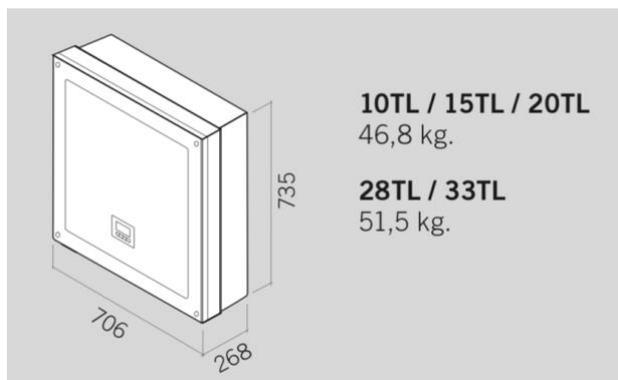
Dimensiones del inversor (mm). Fuente: Ingeteam.
